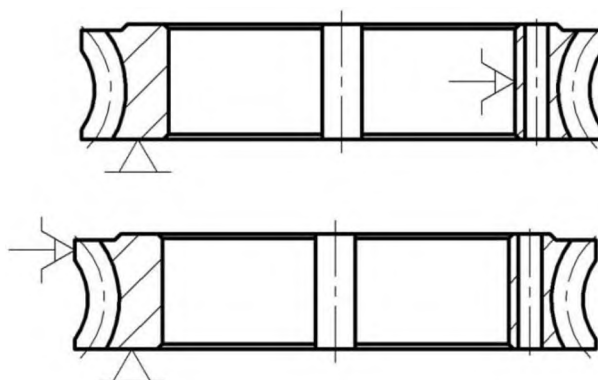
Схема базування на свердлильному, довбальному та зубофрезерному верстатах
